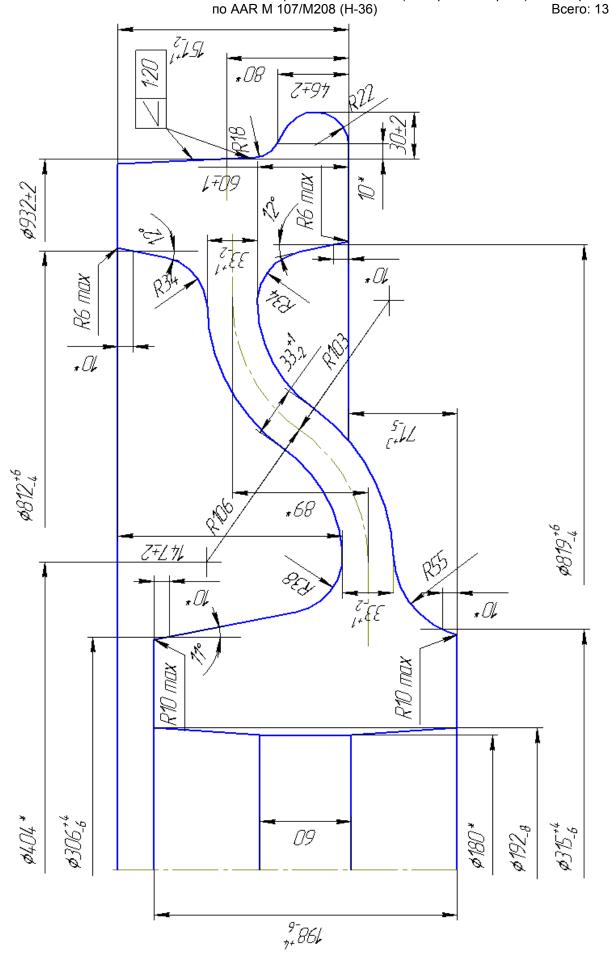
Предварительно обработанное колесо (под чистовое колесо Ø 914,4 мм по вертежу № КР-0055-05А). Маса чернового колеса 453 кг.
